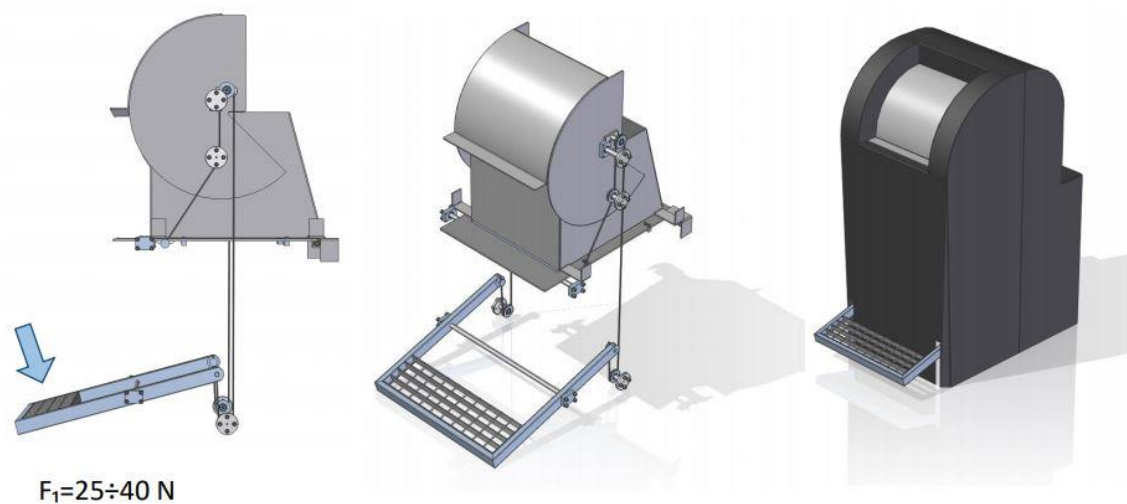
Hlavní konstrukční celky mechanismu [8]
